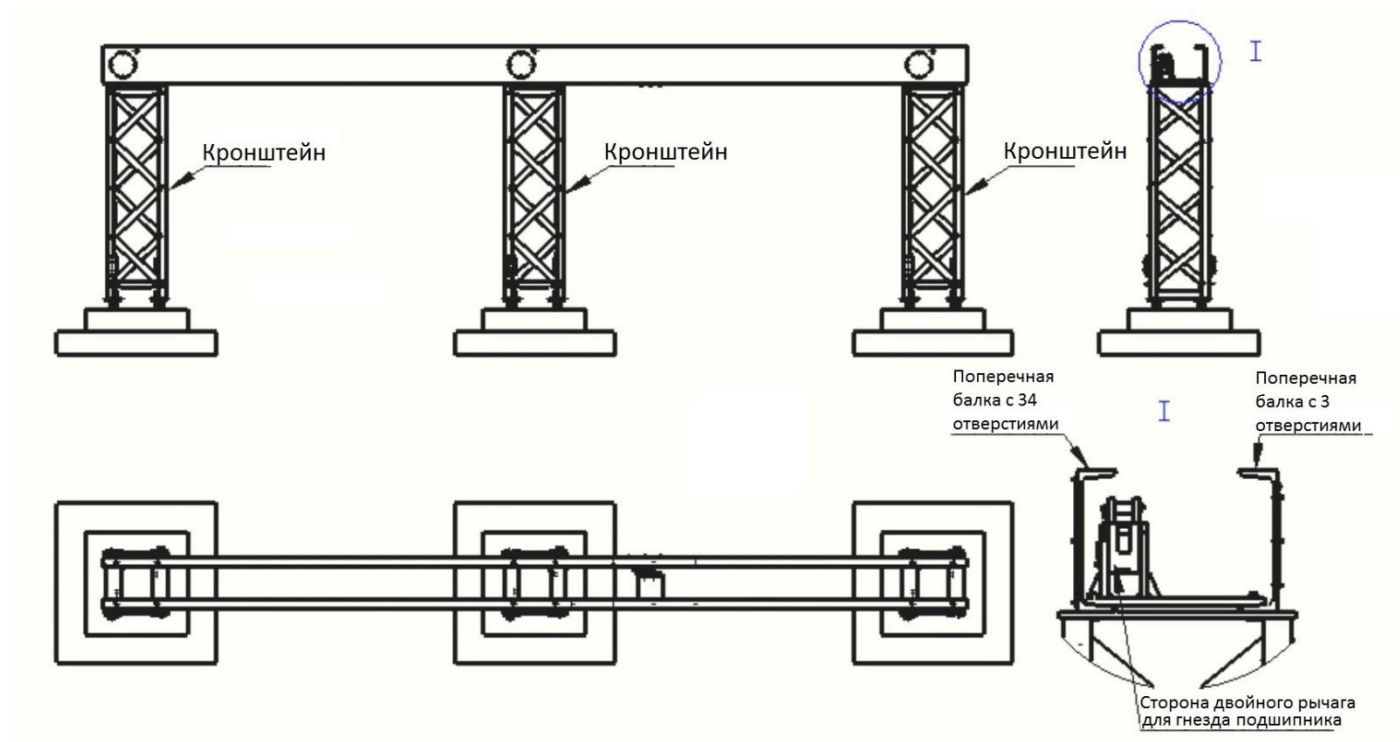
Направление сборки поперечной балки и гнезда подшипника
